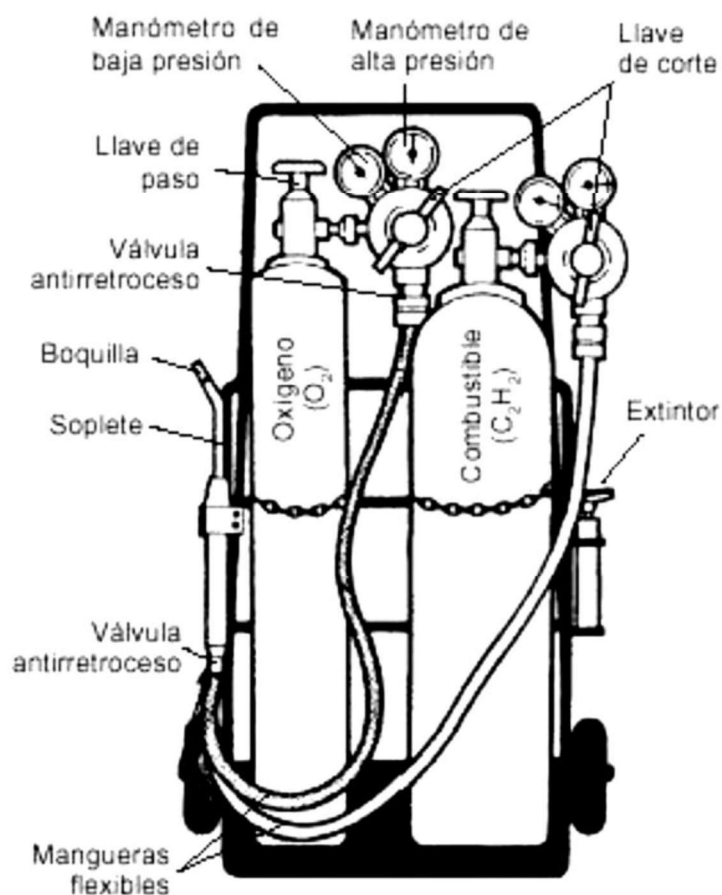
Equipo de suelda oxiacetilénica y sus componentes.
